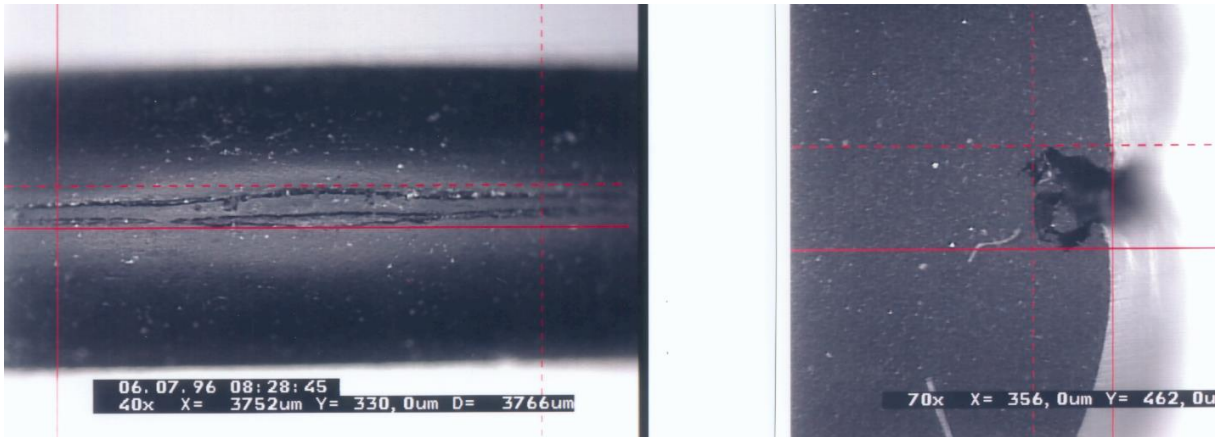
und 14: Schrupfrisse an der Werkzeugtrennebene eines O-Rings und rechts in einem aufgeschnittenen O-Ring
